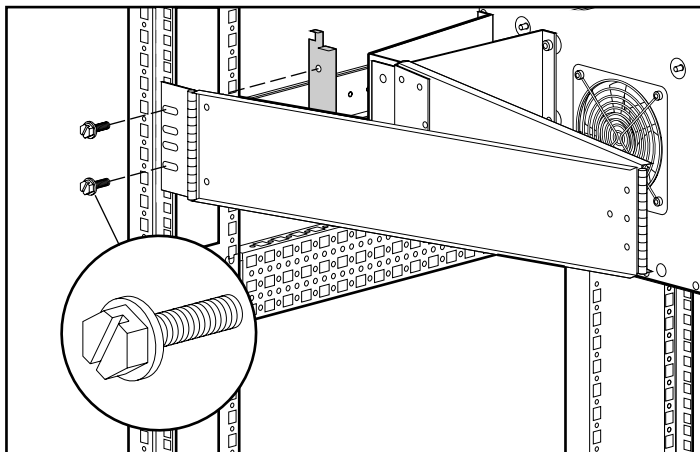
Fissaggio del braccio di supporto dei cavi alla guida del lato verticale
